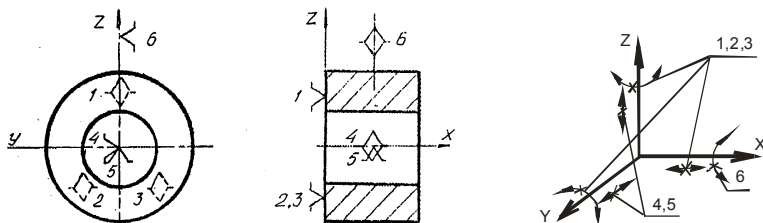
Теоретическая схема базирования заготовки типа диска по оси цилиндрической поверхности отверстия и плоскости
